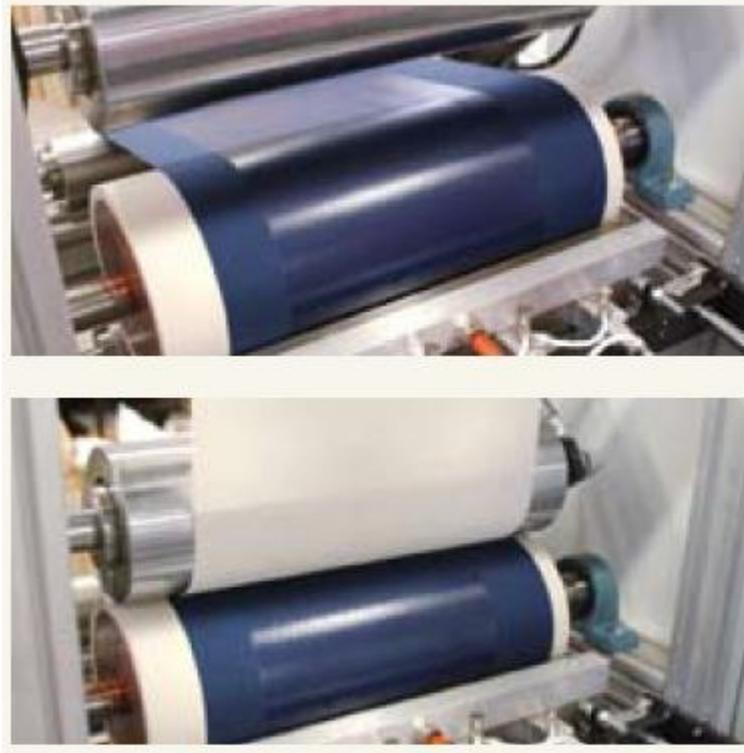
Vista frontal de laminado con membrana o termofilm
